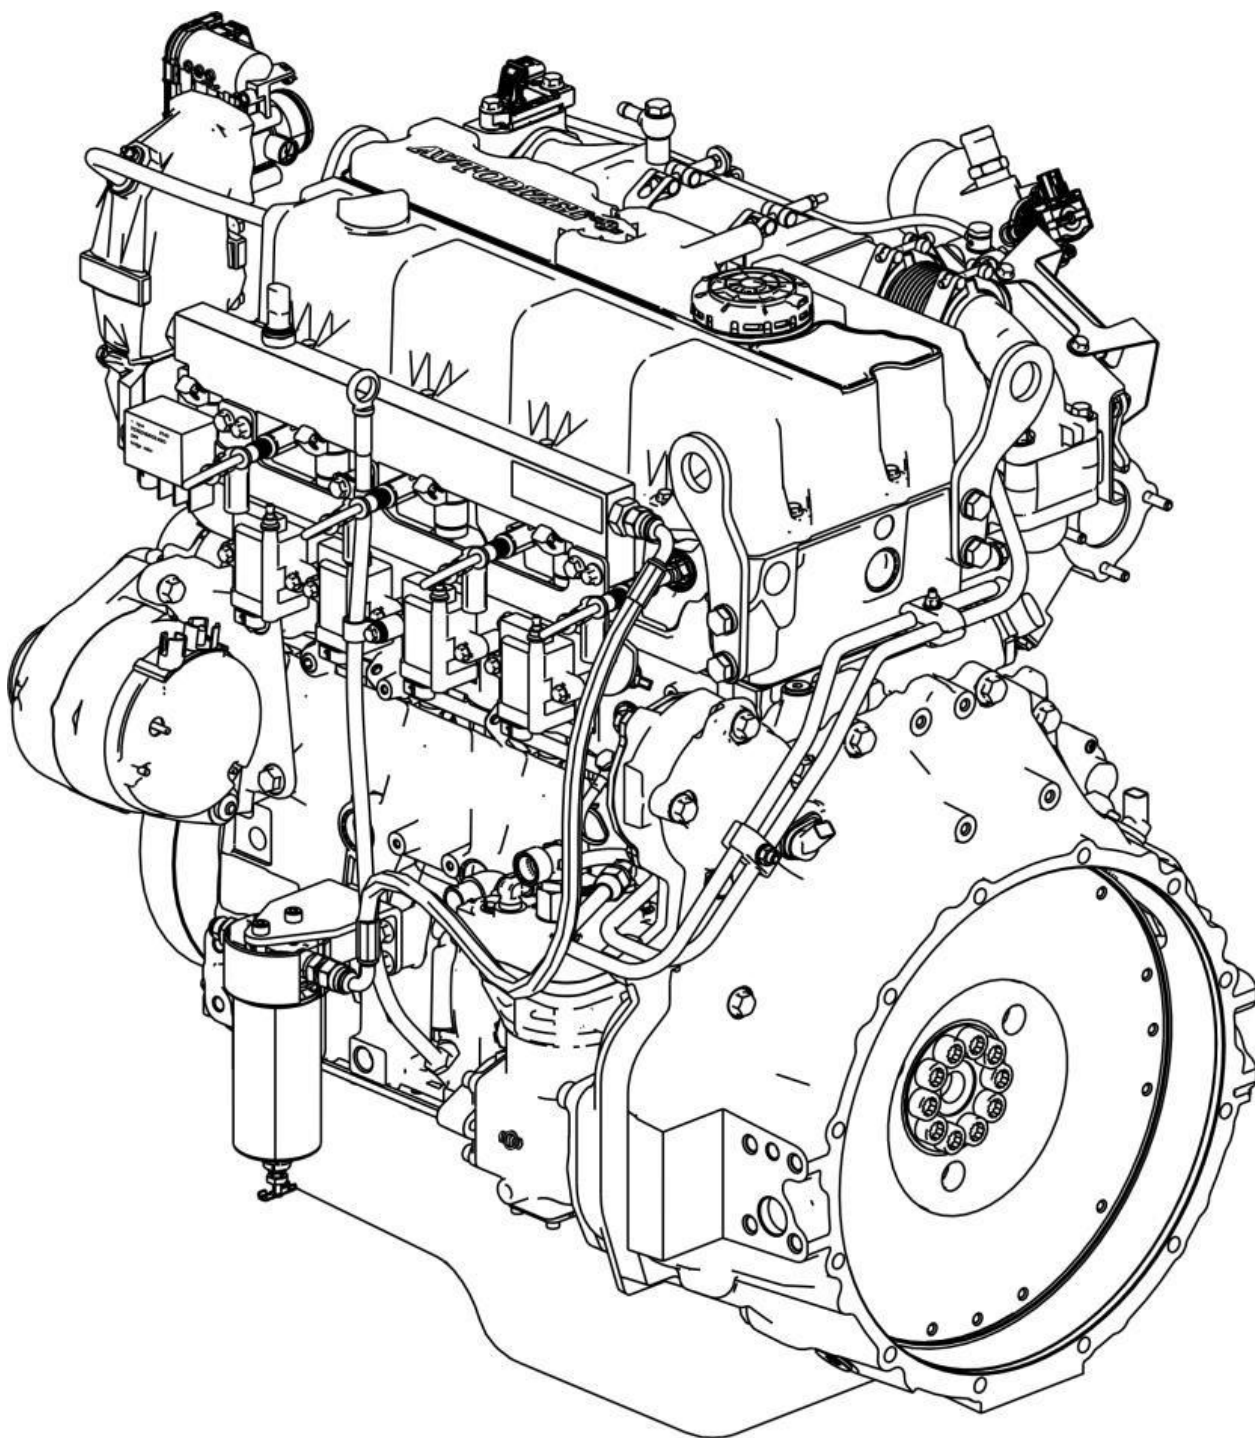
Двигатель ЯМЗ-53414 (общий вид слева)
